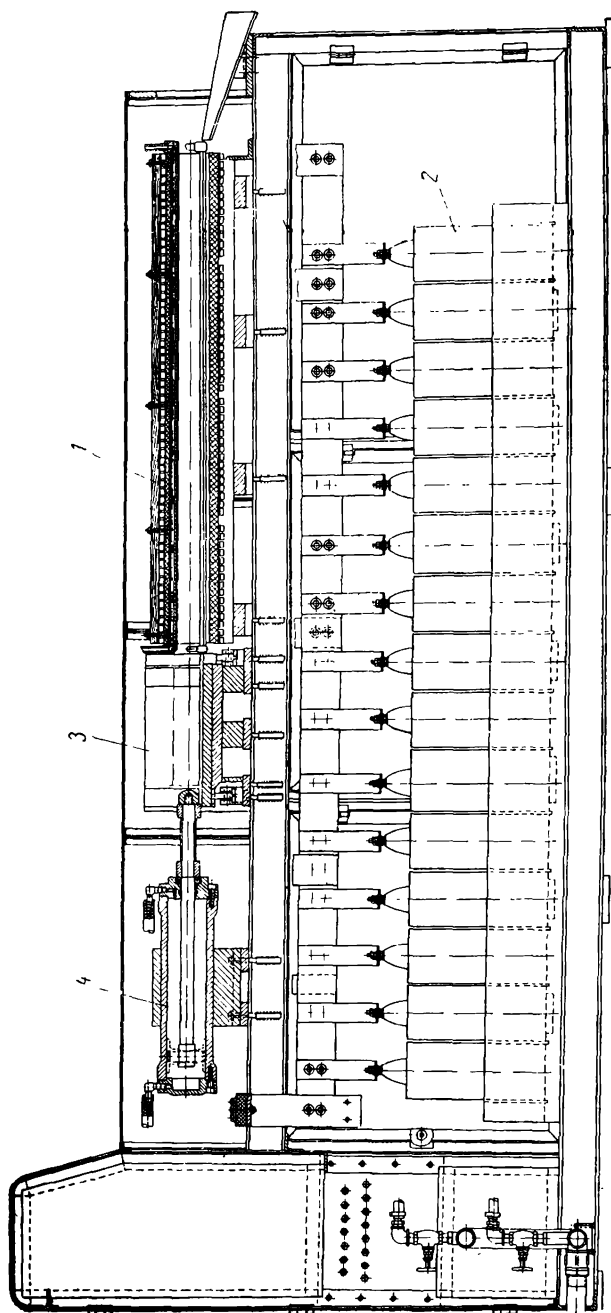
Нагреватель методического действия: 1 — индуктор; 2 — конденсатор; 3 — загрузочная кассета; 4 — пневматический толкатель
